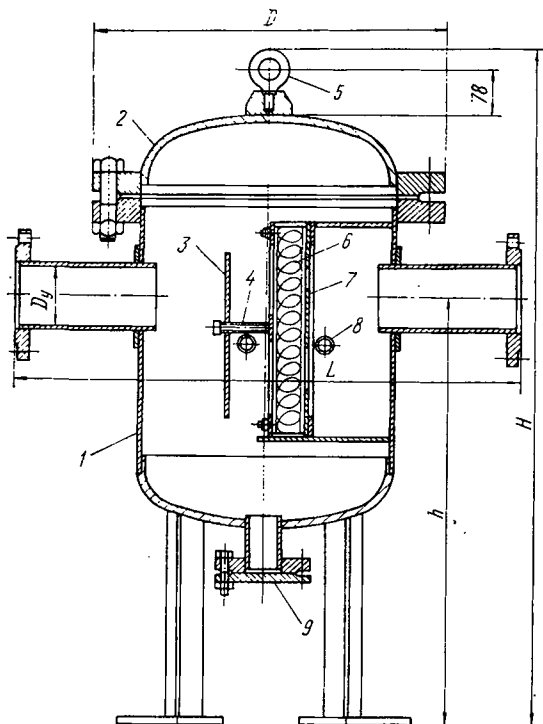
Фильтр кассетный сварной ФГ.
